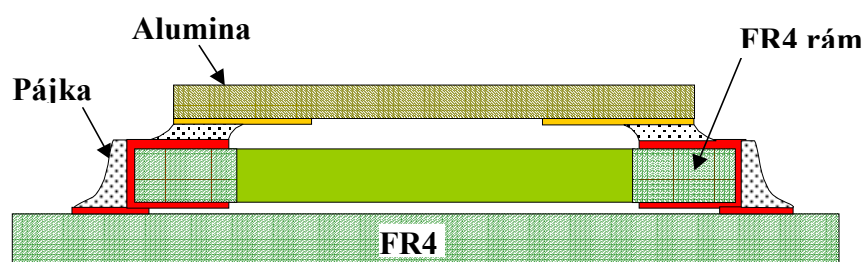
Spojení SMVPH a tvar měřícího vzorku
